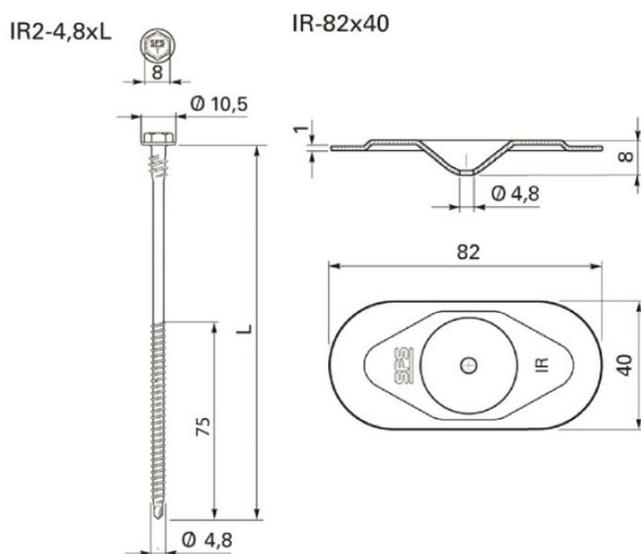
Vis SFS INTEC « IR2 4.8 » fastener + plaquette de fixation IR 82x40
